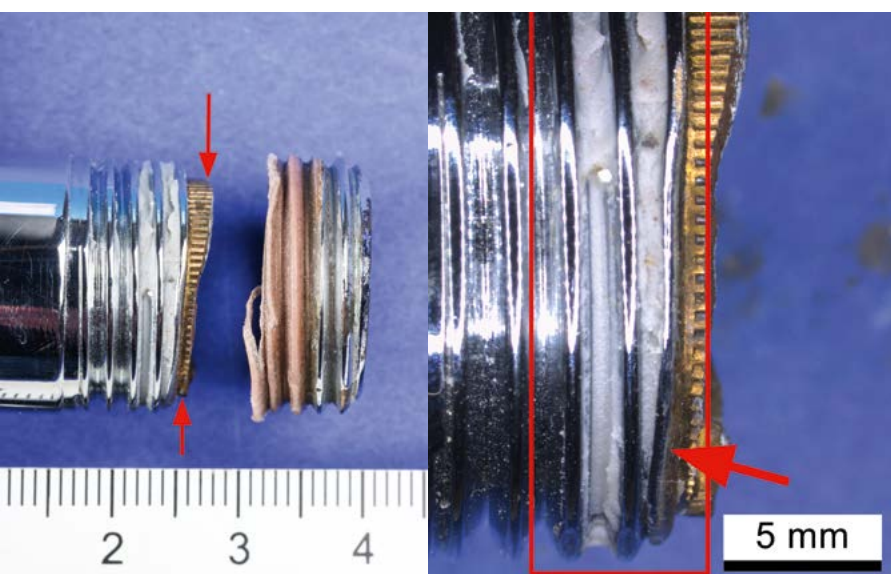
/ Die Bruchstelle liegt in der Nut für den Dichtring. Auf dem Bild rechts ist Dichtpaste in den Gewindekerben zu erkennen.
